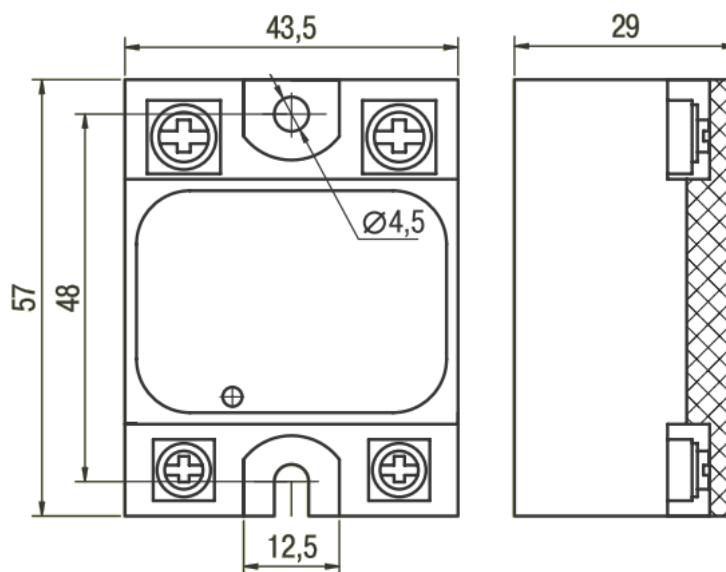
Габаритный чертеж твердотельного реле
